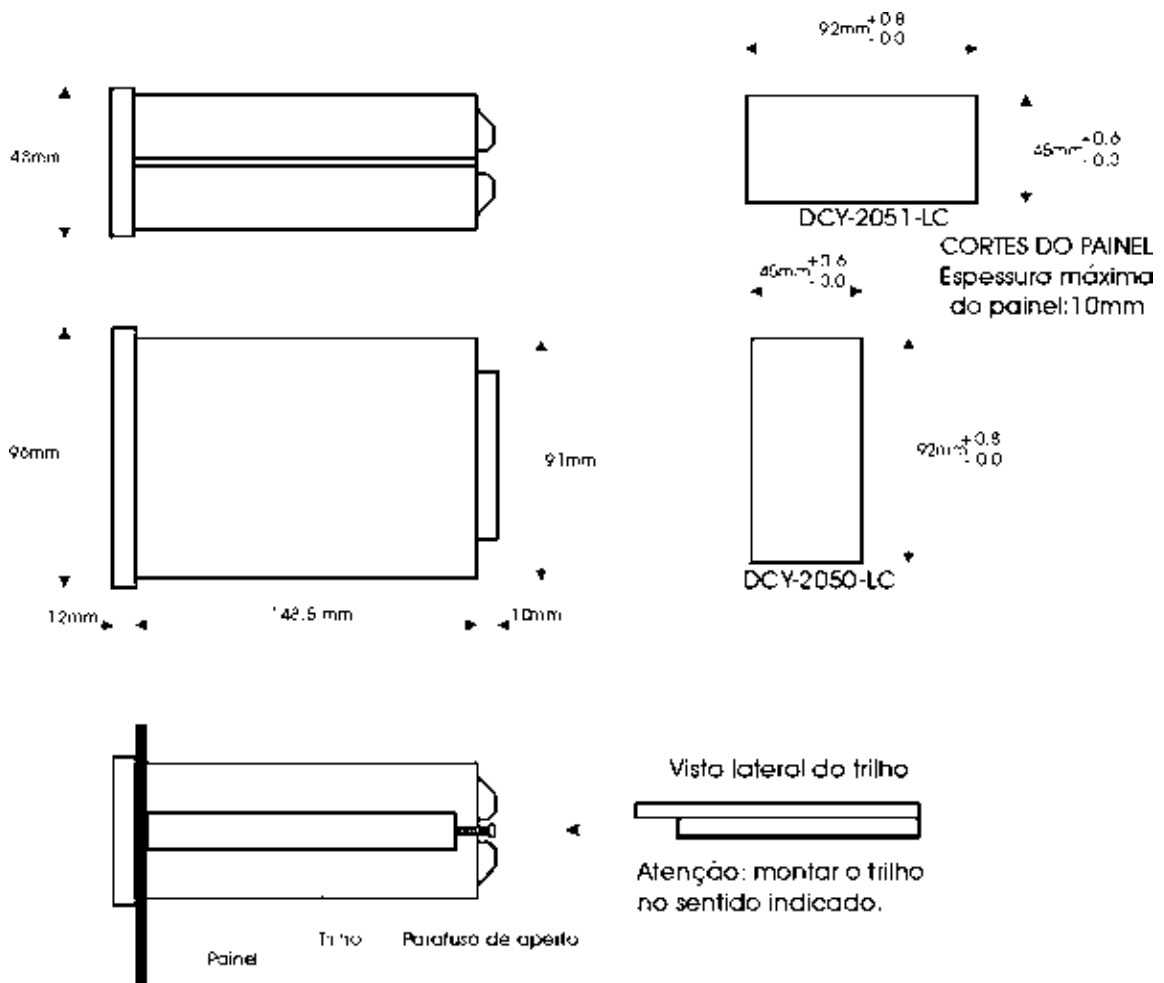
Desenho dimensional, corte e vista lateral da montagem no painel dos controladores DCY-2050/2051-LC.
